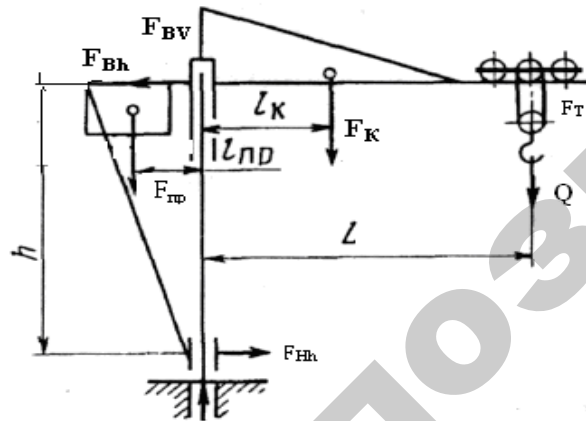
Расчетная схема крана на неподвижной колонне с переменным вылетом стрелы
